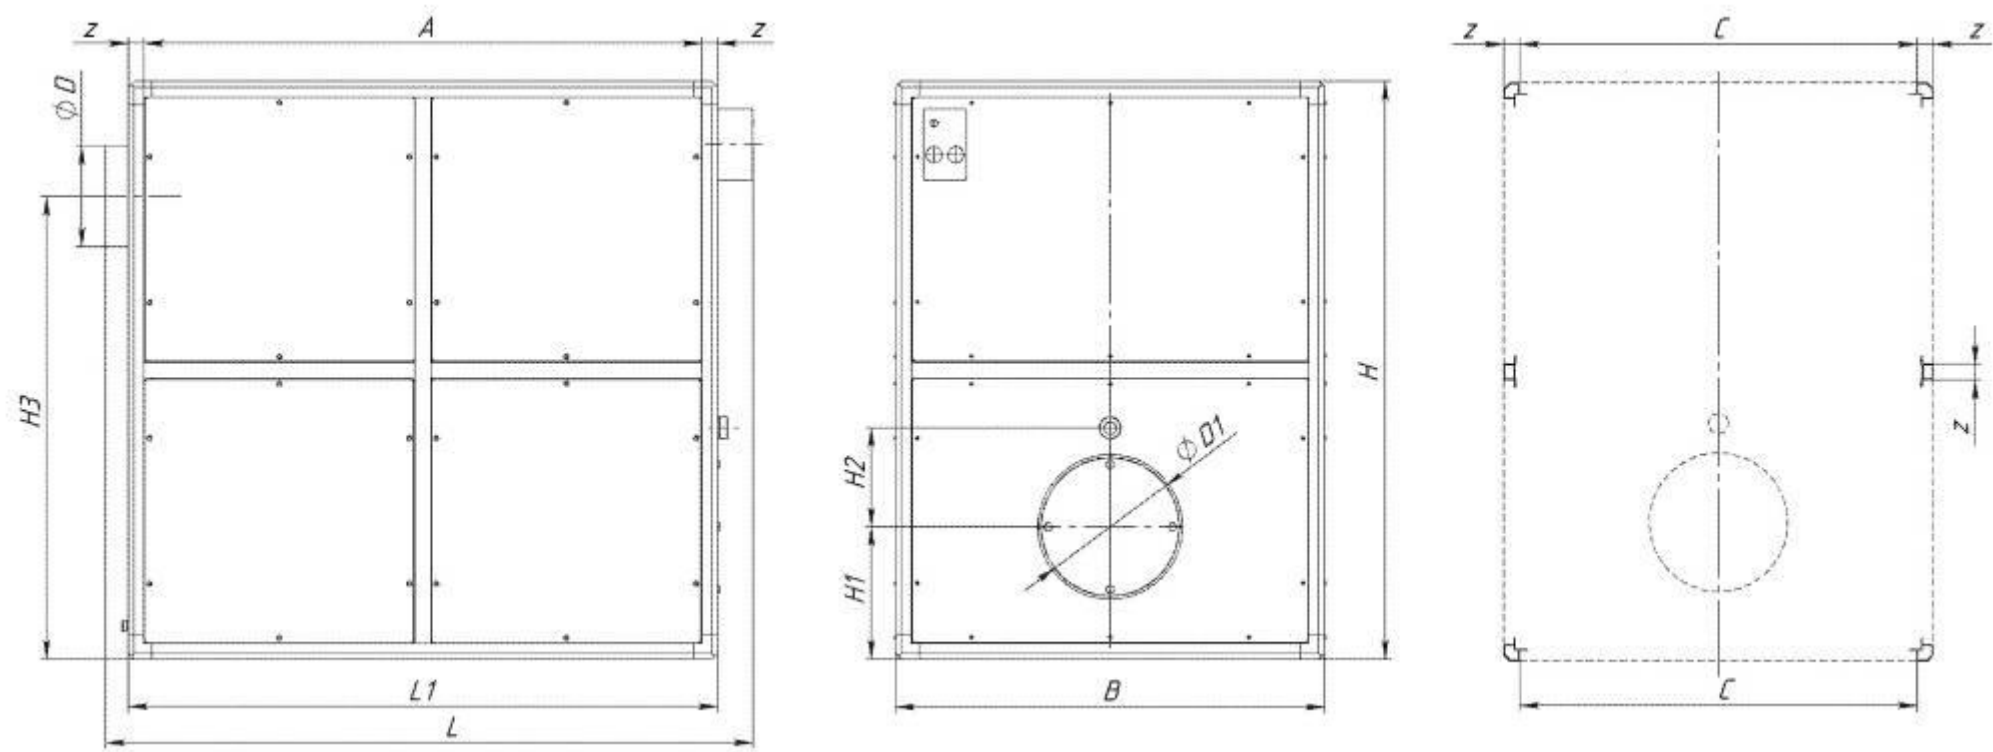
Габаритные размеры воздухонагревателя с секцией вентиляции VBВ
